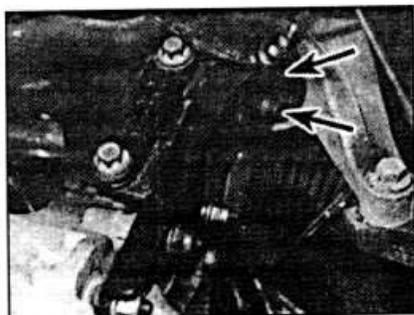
D.15. Расположение болтов подвески установки двигателя и коробки передач.
